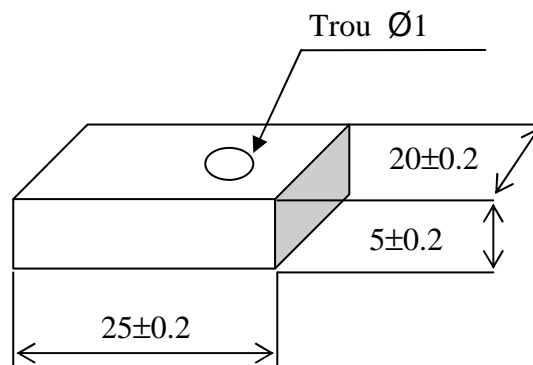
Dimensions de l'éprouvette pour les essais de la masse perdue, mm.
